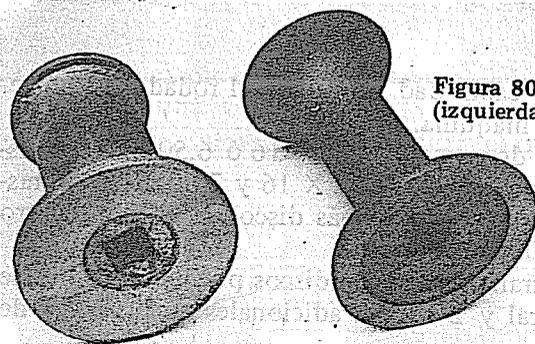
Separador construido en chapa (izquierda) y en hierro fundido (derecha).
